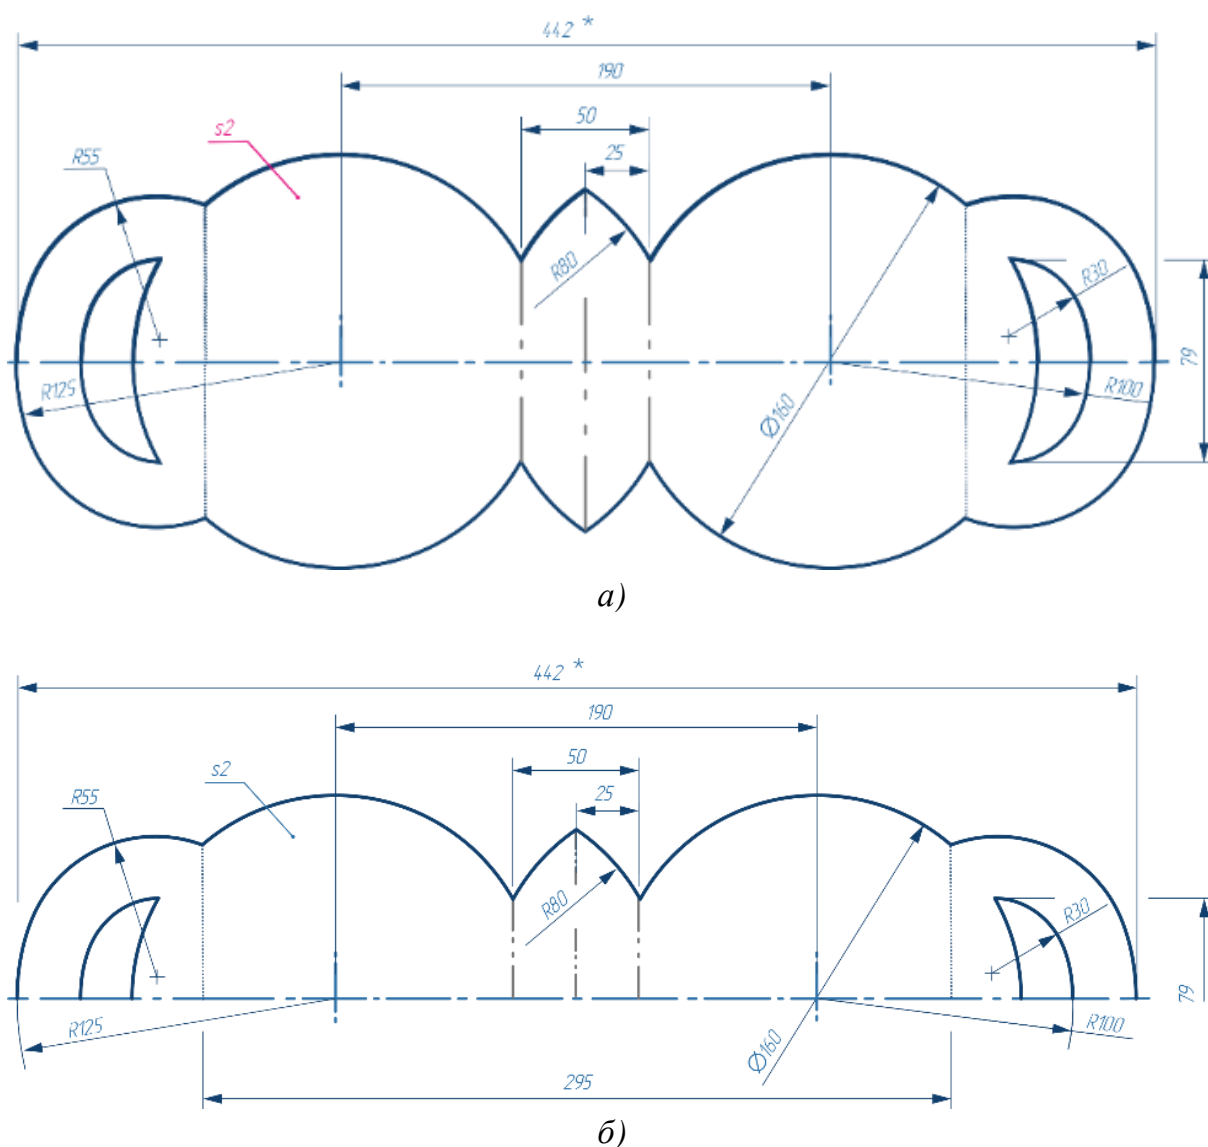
Изображение: а – развертки упаковки для спортивного питания;
